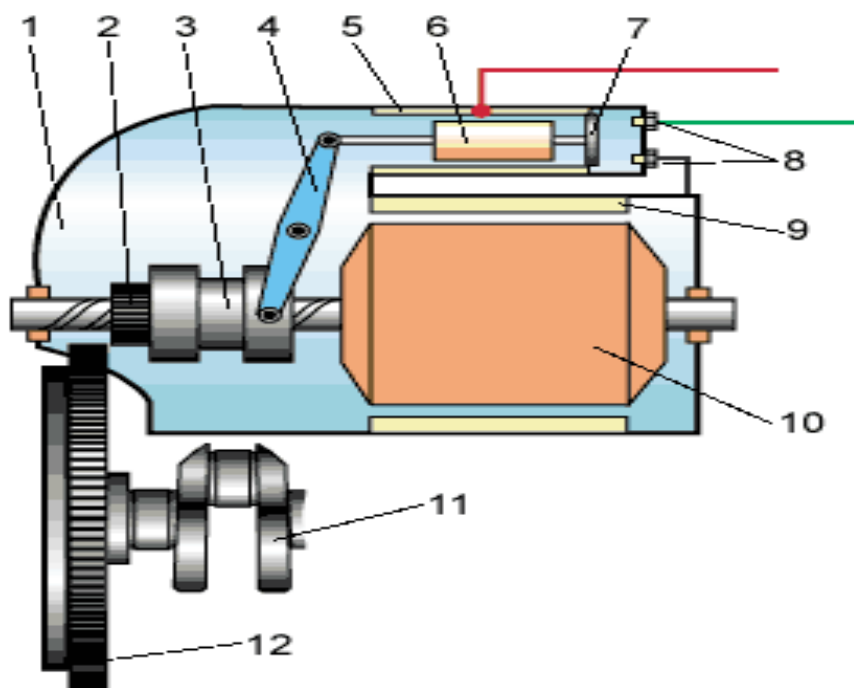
Схема системы пуска двигателя а) стартер выключен 1 - корпус стартера; 2 - вал якоря стартера; 3 - шестерня привода с муфтой свободного хода; 4 - рычаг привода шестерни; 5 - обмотки тягового реле; 6 - якорь тягового реле; 7 - контактная пластина; 8 - контактные болты; 9 - обмотки стартера; 10 - якорь стартера; 11 - коленчатый вал двигателя; 12 - зубчатый венец маховика
